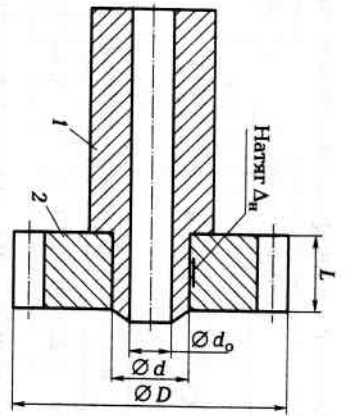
Сборочный чертёж прессового соединения деталей к заданию 7.30
